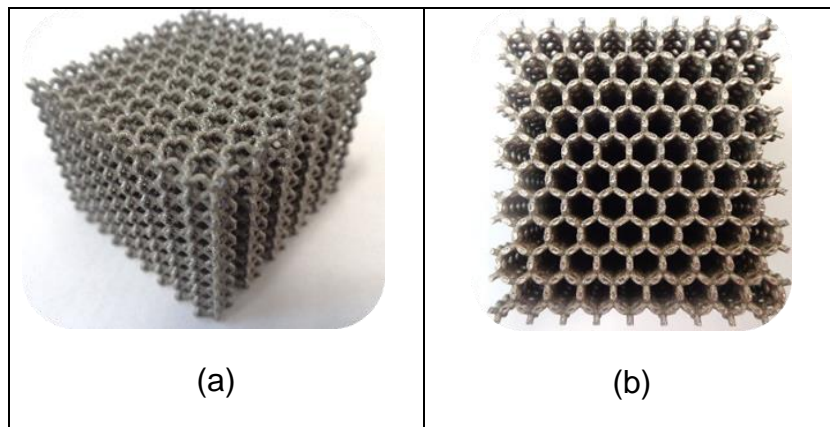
Estructuras fabricadas mediante MA tipo tetragonal, (a) Vista isométrica (b) vista superior
